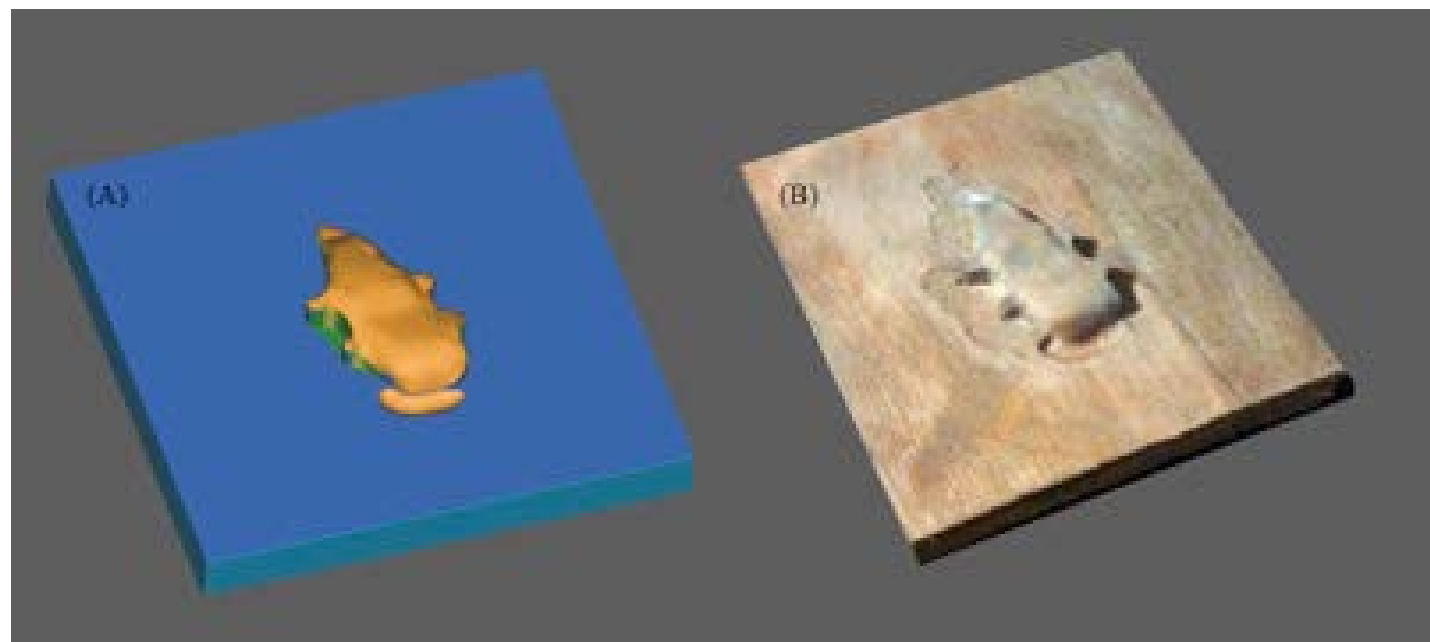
(A) Molde para estampagem virtual; (B) Molde para estampagem usinado. Acervo Pessoal. IFPB, 2016
